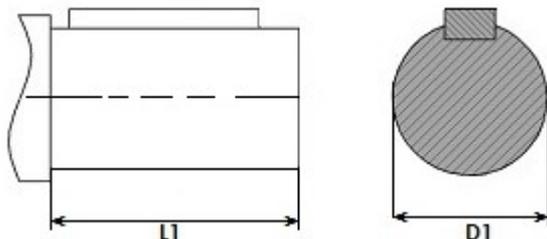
Замеры диаметра и длины вала электродвигателя.
